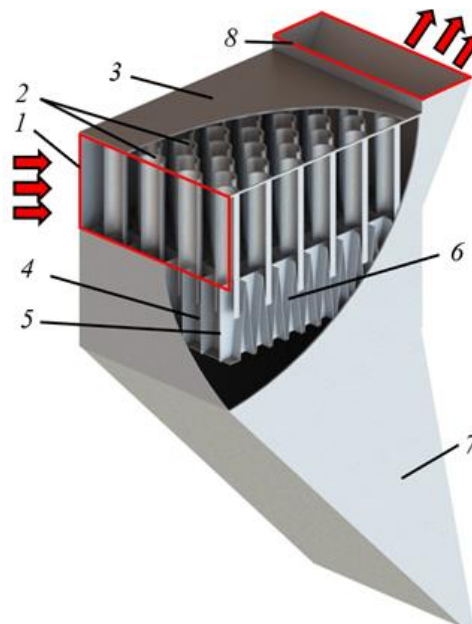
Трехмерная модель сепарационного устройства с дугообразными элементами (вид с местными разрезами): 1 – входной патрубок; 2 – дугообразные элементы; 3 – корпус; 4 – сепарационная решетка; 5 – продольные пластины; 6 – поперечные V-образные пластины; 7 – бункер; 8 – выходной патрубок
